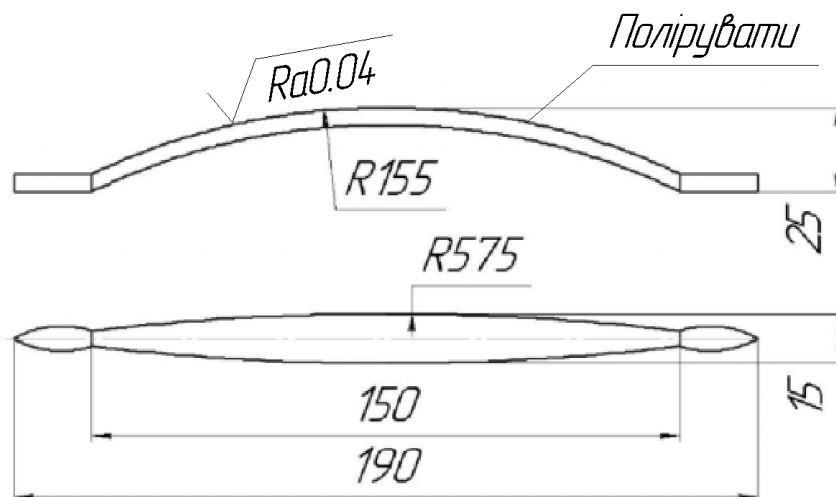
Ескіз деталі з вимогами до якості обробленої поверхні
